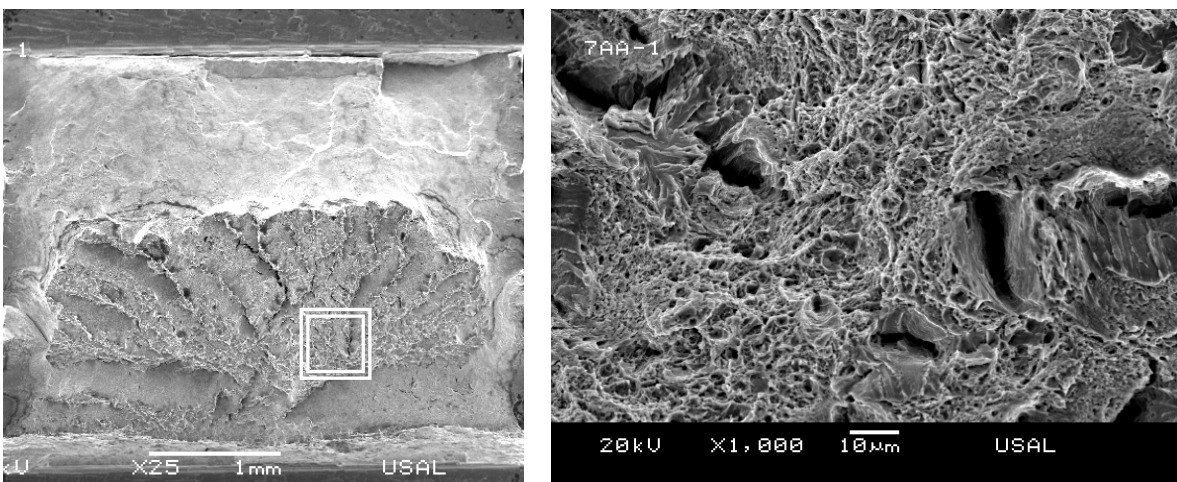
Fractografía de la zona de proceso de fractura de la probeta B7-AA-1.
